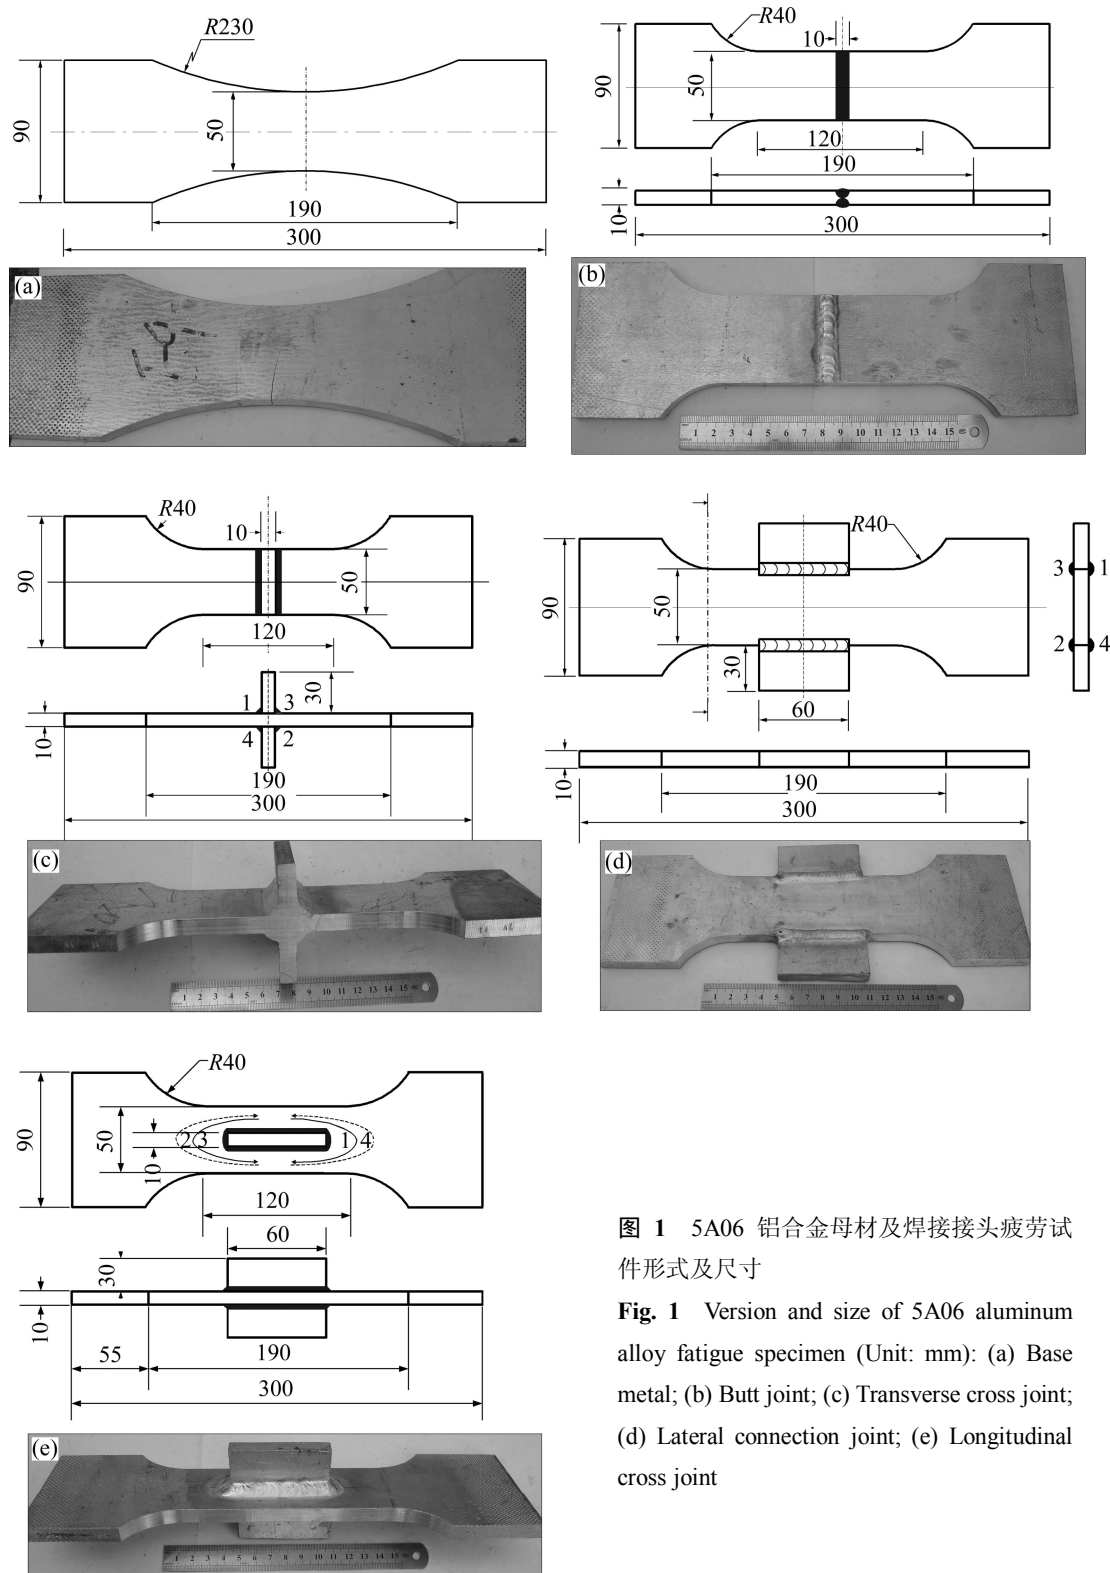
5A06 铝合金母材及焊接接头疲劳试件形式及尺寸
